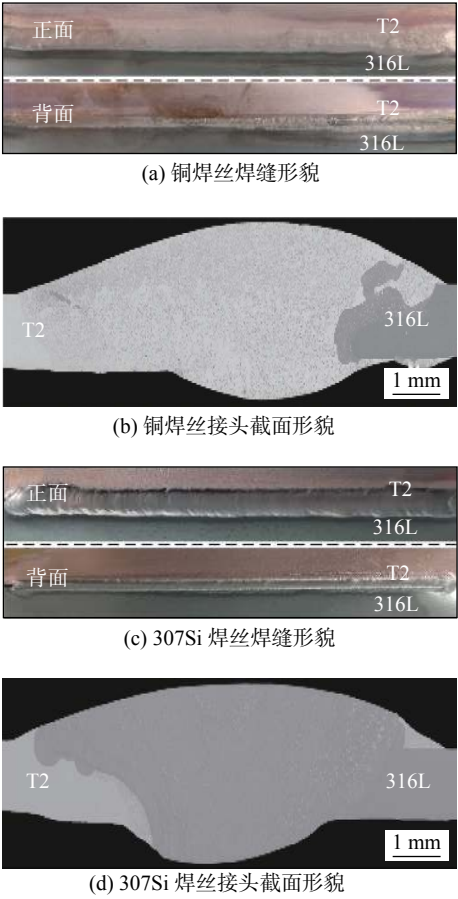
两种焊丝制备焊缝的宏观形貌
